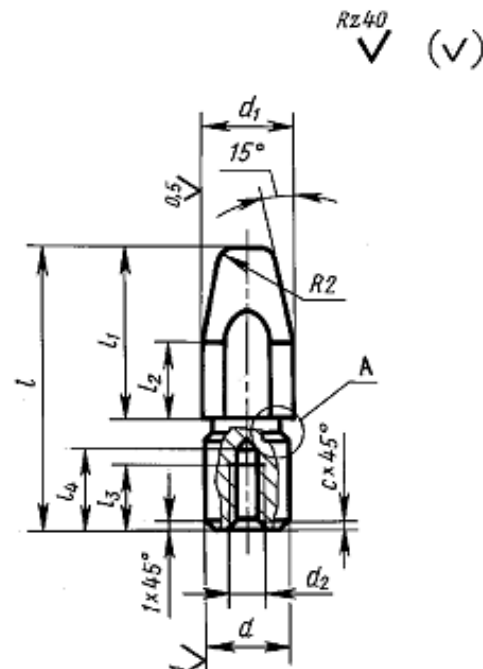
Направляющий штырь с резьбовым отверстием
